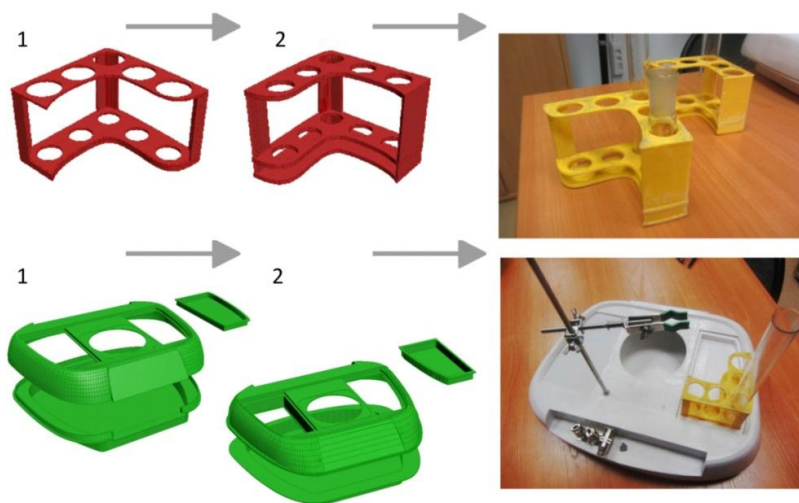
3D прототипирование держателя для пробирок и основного корпуса прибора
